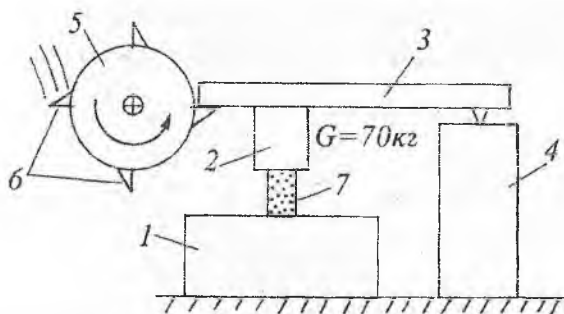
Схема рычажного молота: 1 - наковальня, 2 - молот  $G=70\text{кг}$ , 3 - молотовище, 4 - стойка, 5 - водяное колесо, 6 - кулаки, 7 - заготовка
